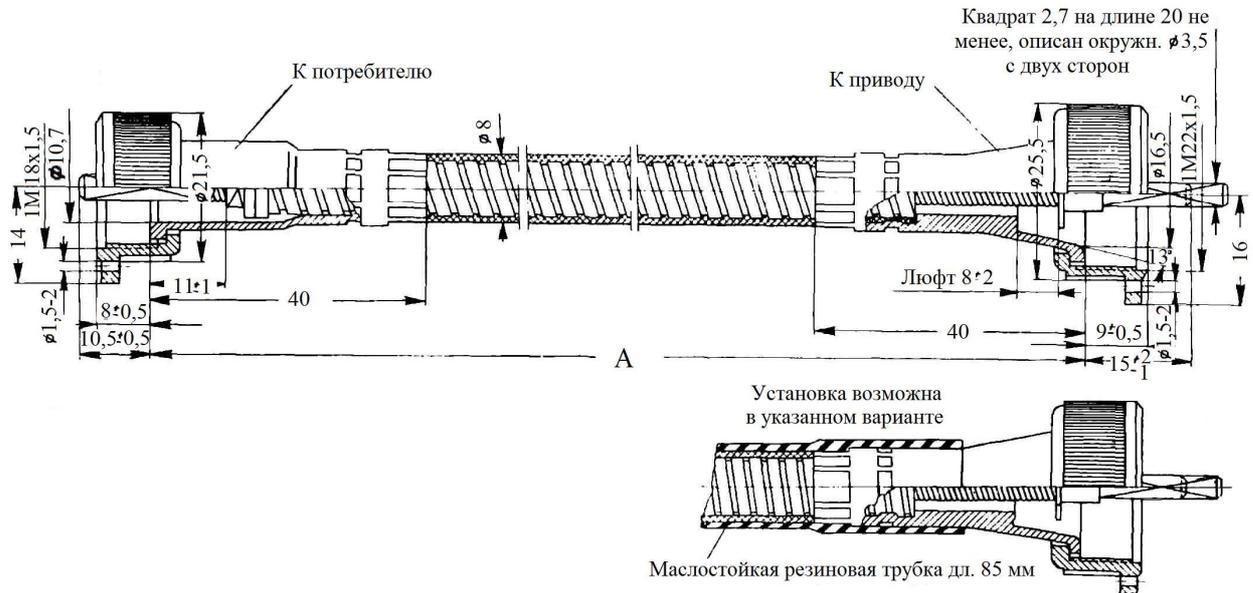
Гибкий вал ГВН-20В, габаритные размеры
